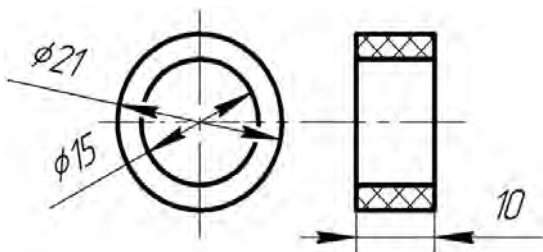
Эскиз кольцевых образцов для испытаний на растяжение
